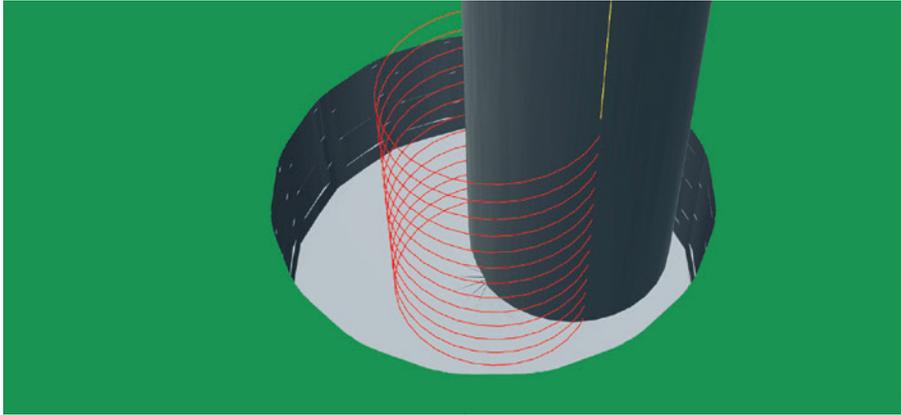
Besonders schonend für Werkzeug und Werkstück: das Eintauchen auf einer Helixbahn
